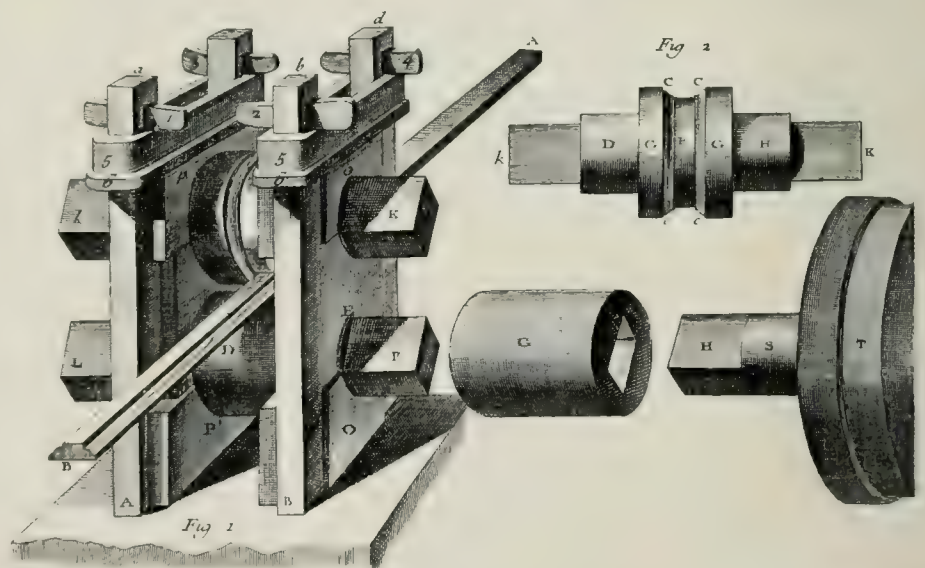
Façonwalzwerk (Diderot et d'Alembert, Encyclopédie, 1773, Planches III, 137).
